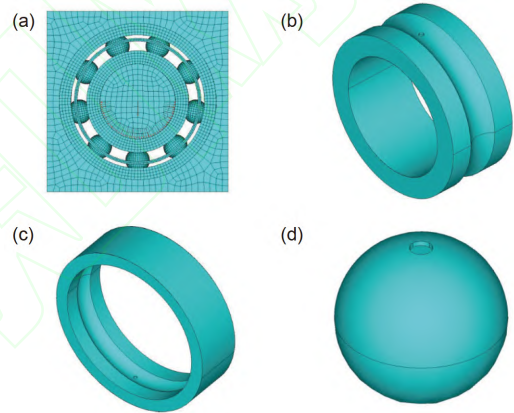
(网络版彩图)故障轴承有限元模型. (a) 轴承; (b) 内圈故障; (c) 外圈故障; (d) 滚动体故障
